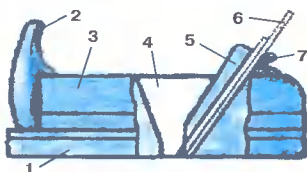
Обычный столярный рубанок: 1 — подошва, 2 — рукоятка, 3 — корпус, 4 — леток, 5 — клин, 6 — нож, 7 — упор.
